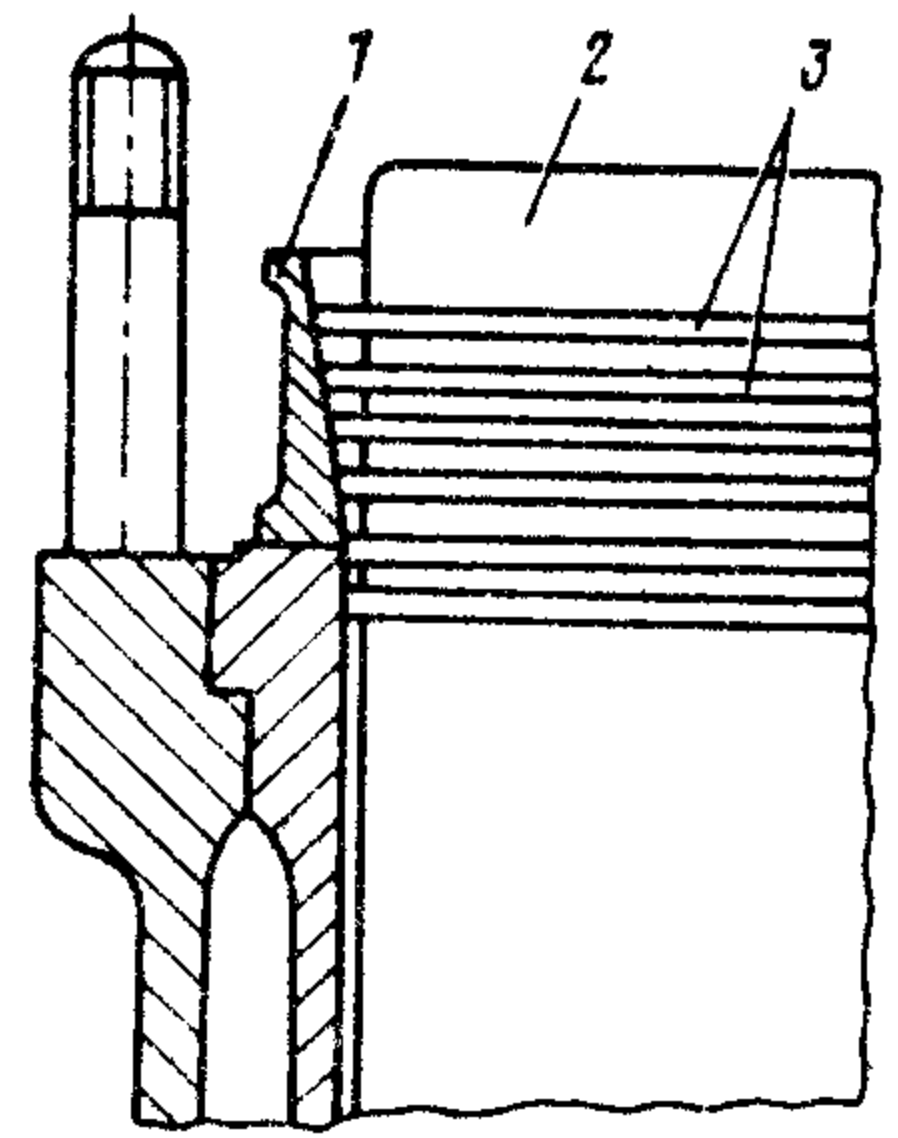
Приспособление для установки поршня в сборе с кольцами в цилиндр
